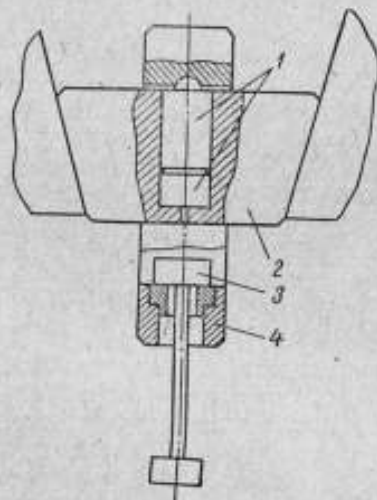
Приспособление для испытания на растяжение с упруго-контактным динамометром (1 — динамометр, 2 — клиновой вкладыш, 3 — образец, 4 — хомут).
